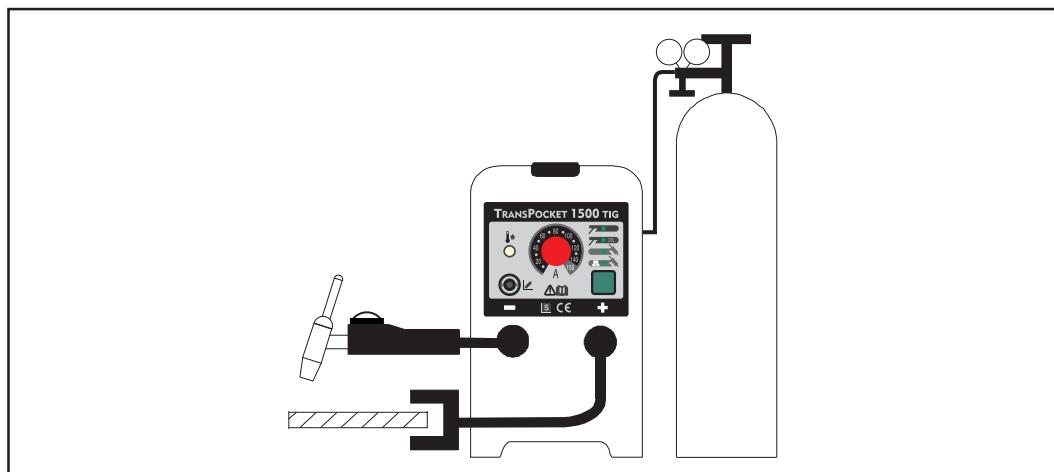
TP 1500 TIG equipado com o queimador de soldadura AL 1500
